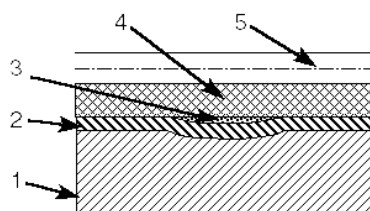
Строение лакокрасочного покрытия: 1 - окрашиваемая поверхность; 2 - грунтовка; 3 – местная шпатлёвка; 4 – общая шпатлёвка (порозаполнитель); 5 – слой покрывной эмали.
